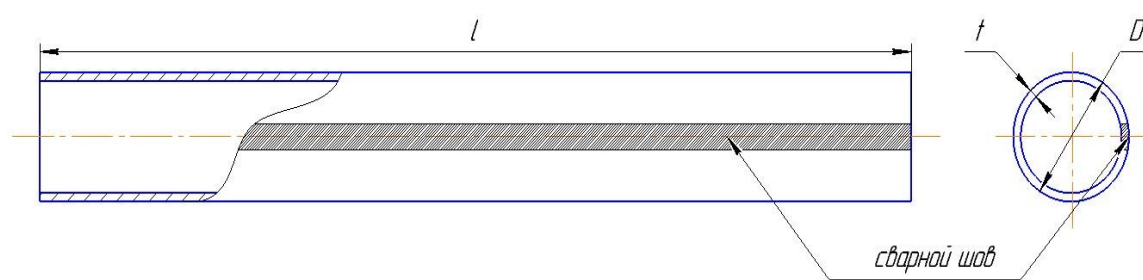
Общий вид электросварной прямошовной трубной заготовки (эскиз).
